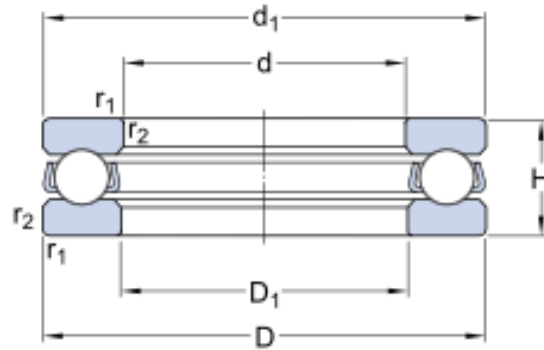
Desenho técnico do rolamento axial de esferas, escora simples 51101 da SKF.
